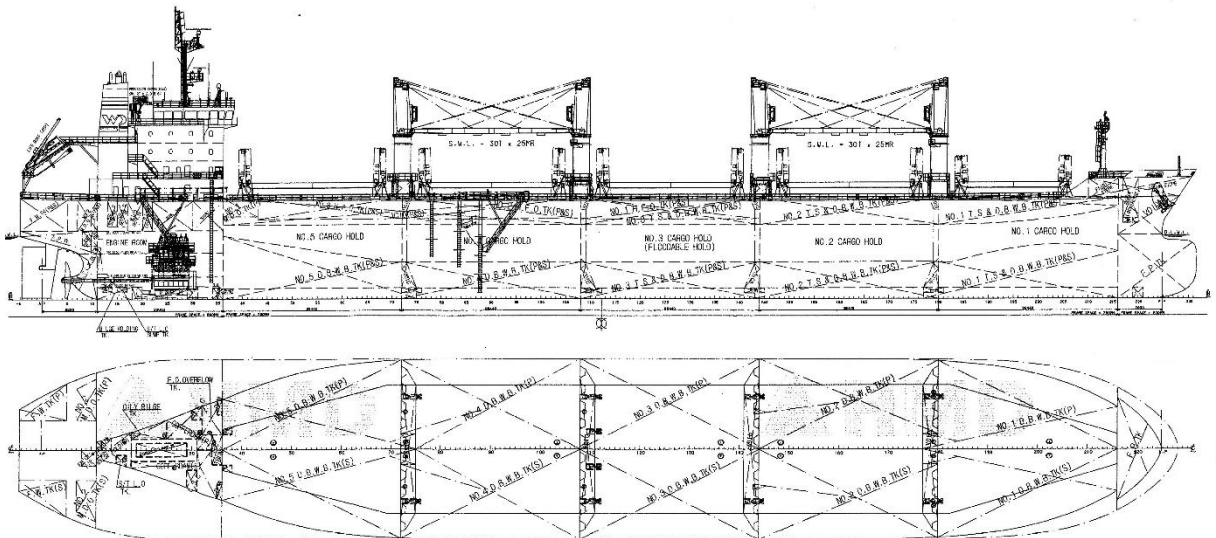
Загальний вигляд балкера “NORD TOKYO”
